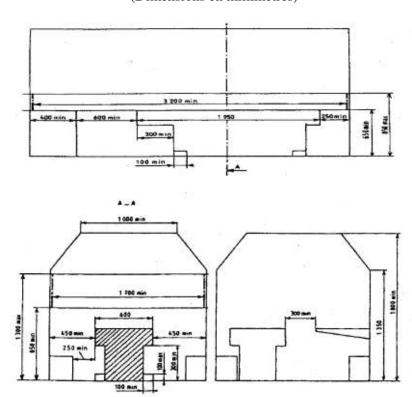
Dimensions intérieures exigées (Dimensions en millimètres)
